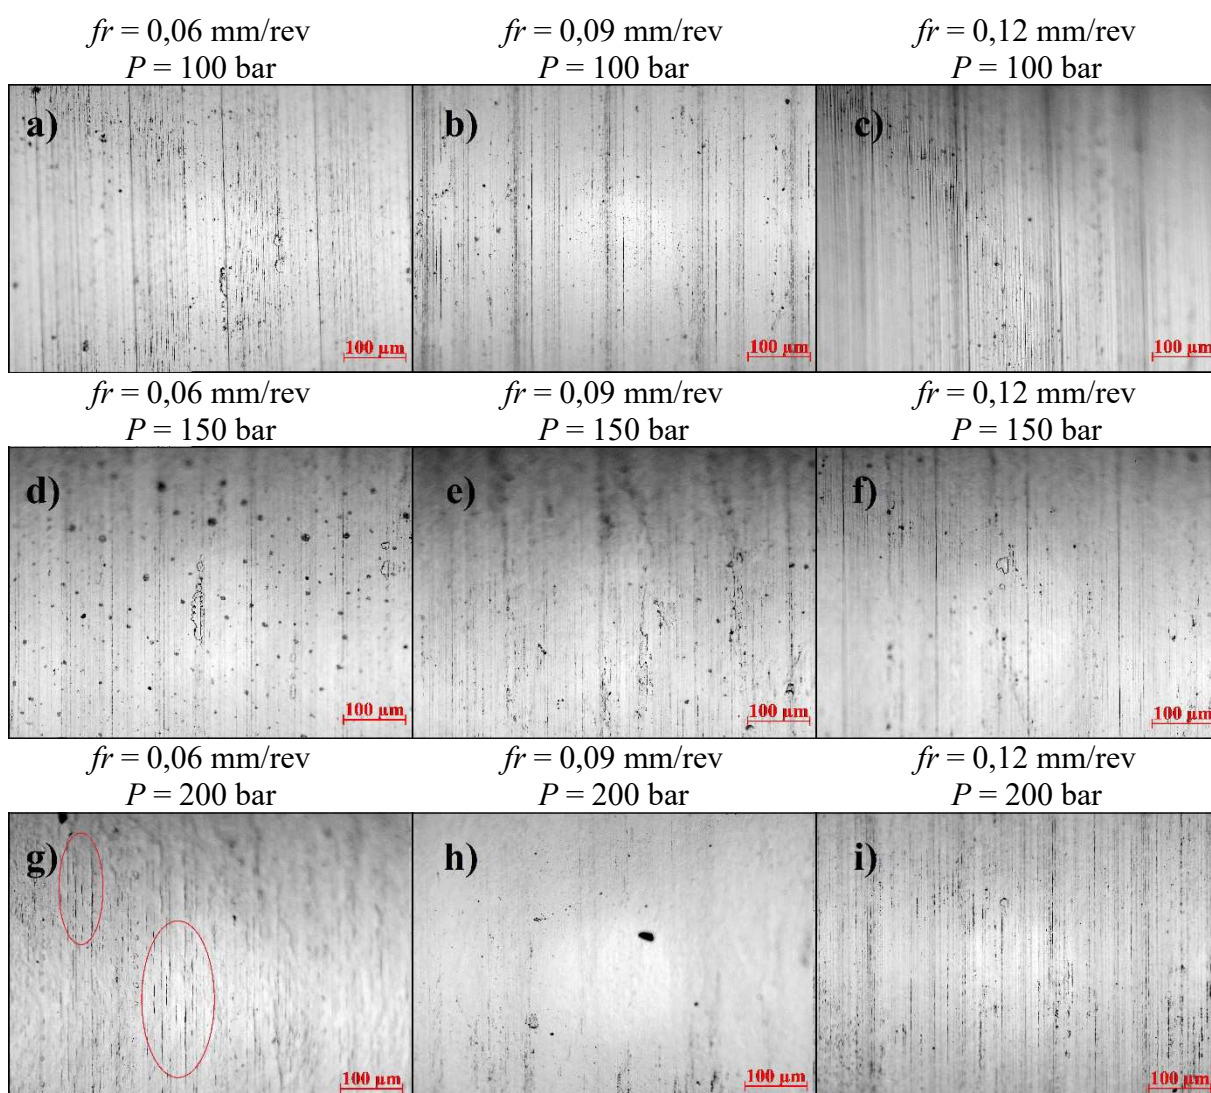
Superfícies de amostras torneadas com R_a -torneado = 0,80 μ m após roleteamento: a) $f_r = 0,06$ mm/rev e $P = 100$ bar, b) $f_r = 0,09$ mm/rev e $P = 100$ bar, c) $f_r = 0,12$ mm/rev e $P = 100$ bar, d) $f_r = 0,06$ mm/rev e $P = 150$ bar, e) $f_r = 0,09$ mm/rev e $P = 150$ bar, f) $f_r = 0,12$ mm/rev e $P = 150$ bar, g) $f_r = 0,06$ mm/rev e $P = 200$ bar, h) $f_r = 0,09$ mm/rev e $P = 200$ bar e i) $f_r = 0,12$ mm/rev e $P = 200$ bar.
